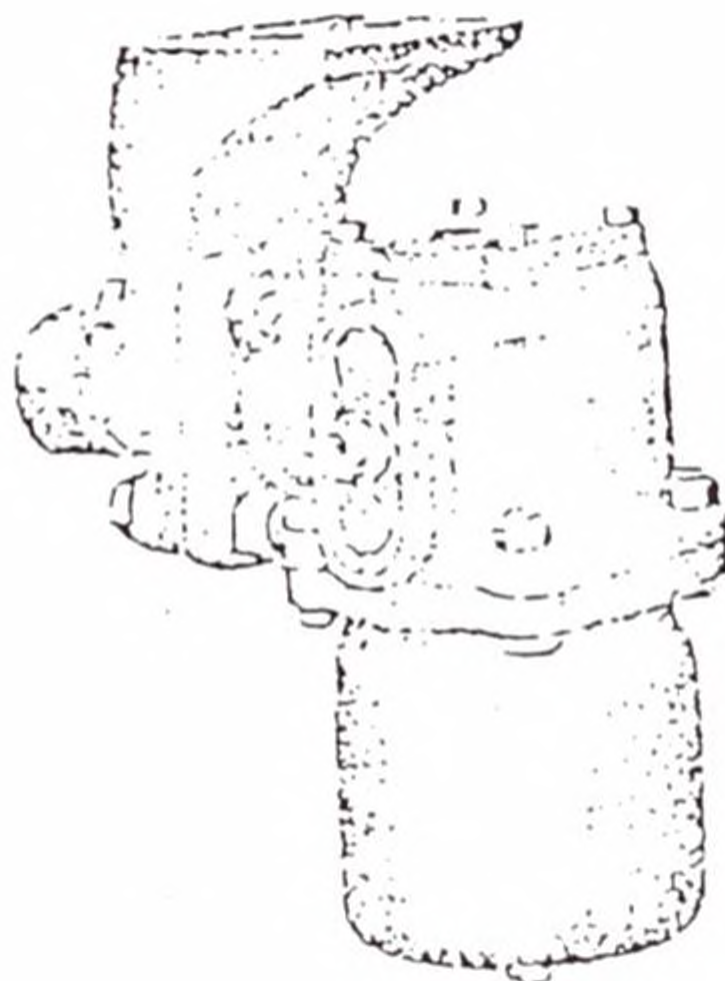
VALVULA DE DESCARGA KM CON SOPORTE LARGO PARA MONTAJE.
